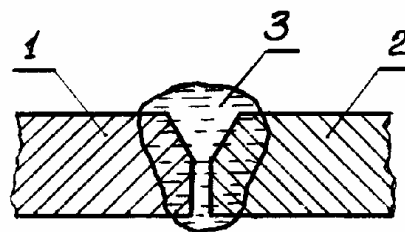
Схема образования шва при сварке плавлением.
